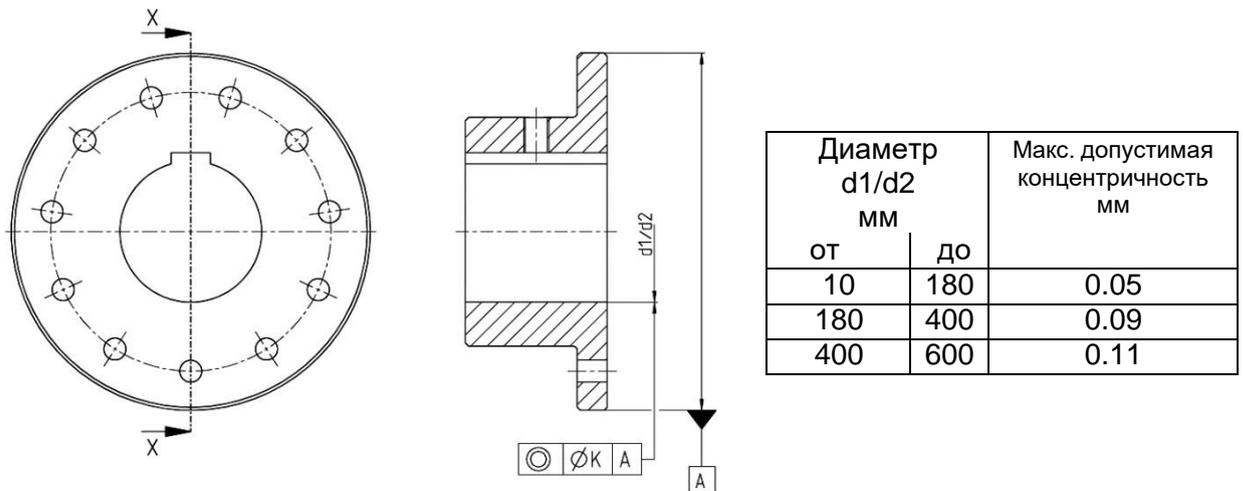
Допуск формы и положения отверстия и положения шпоночного паза.
